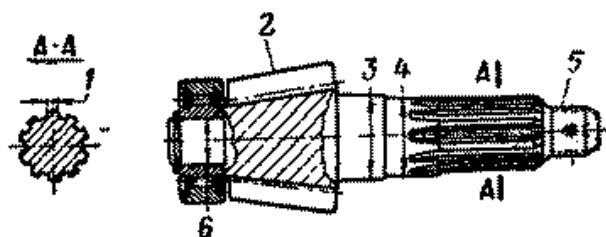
Ведущая шестерня главной пары с подшипником в сборе
